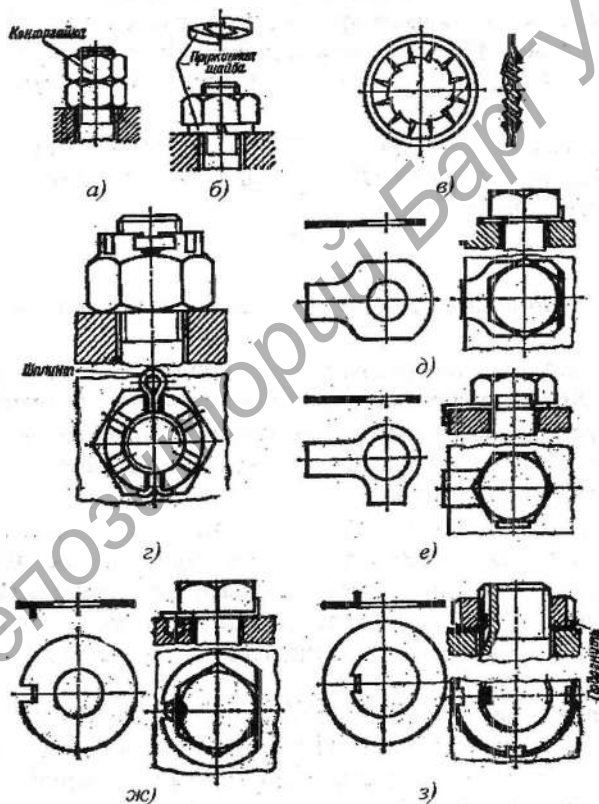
Замки общего назначения [3, с. 75]
